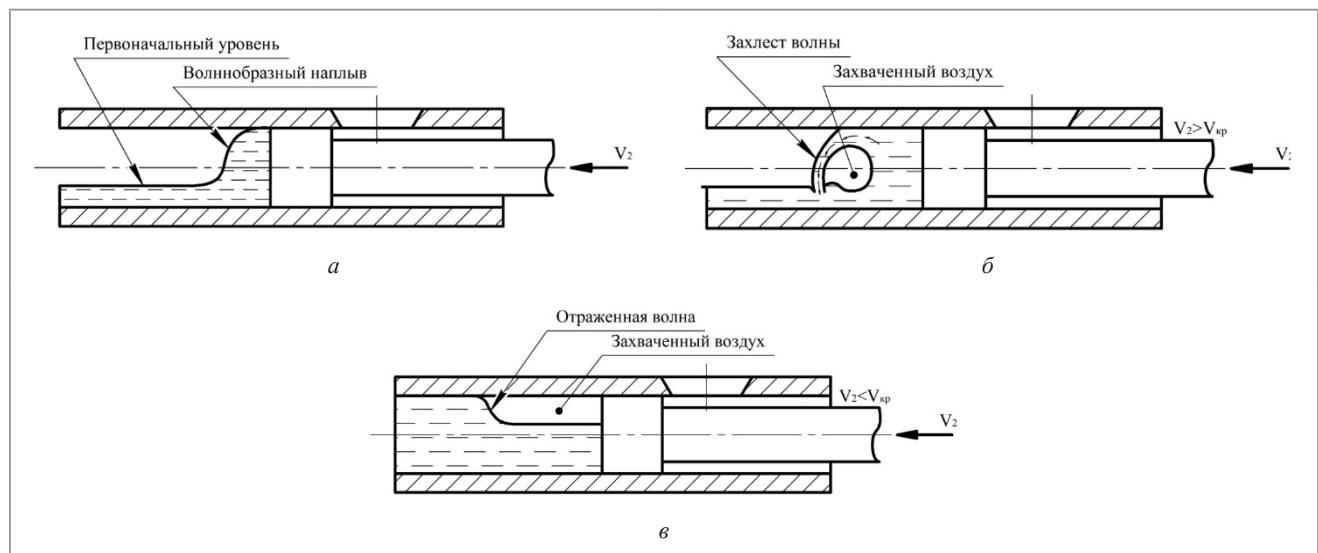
Движение поршня и расплава в камере прессования при литье под давлением:
